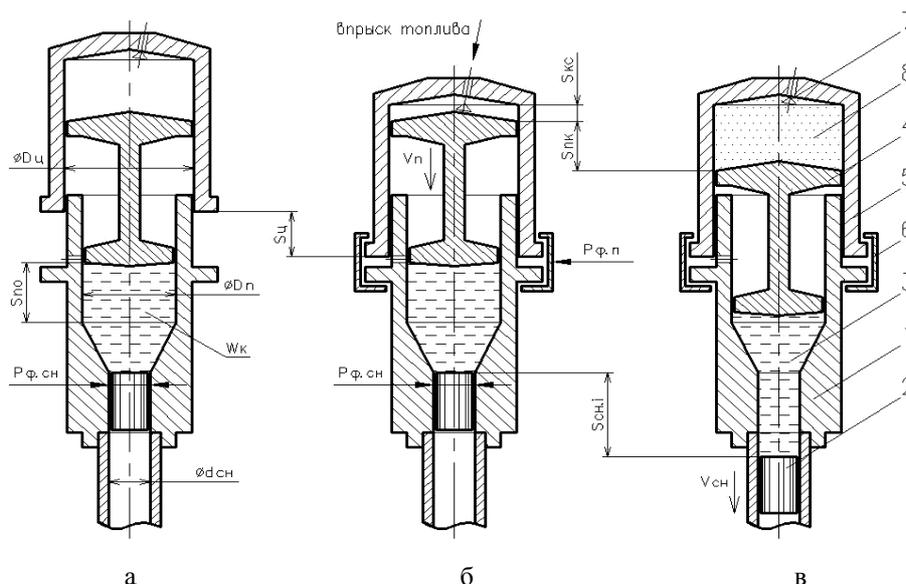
Схема разгонного устройства для гидродинамической штамповки
